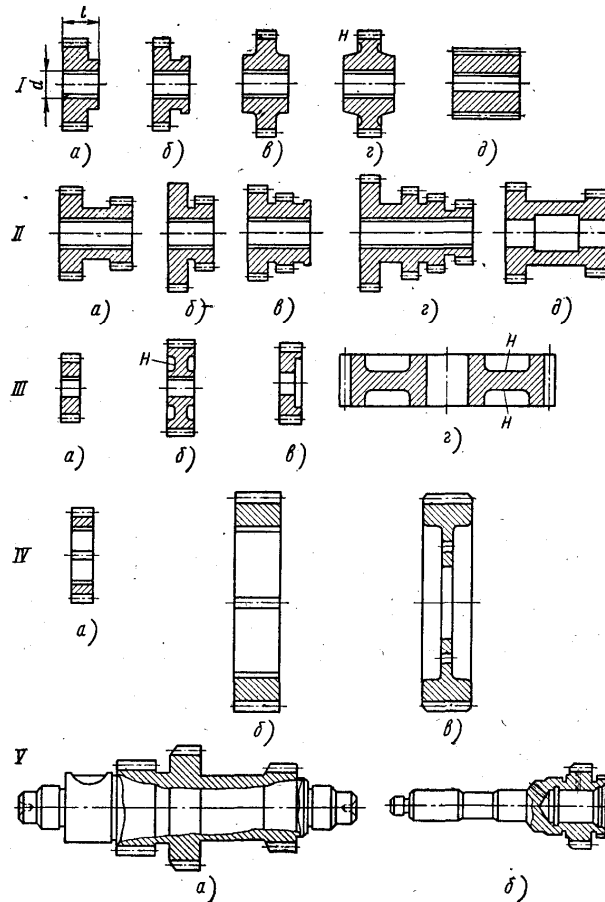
Различные типы цилиндрических зубчатых колес: 1—V — типы, а—д — конструктивные разновидности каждого типа
